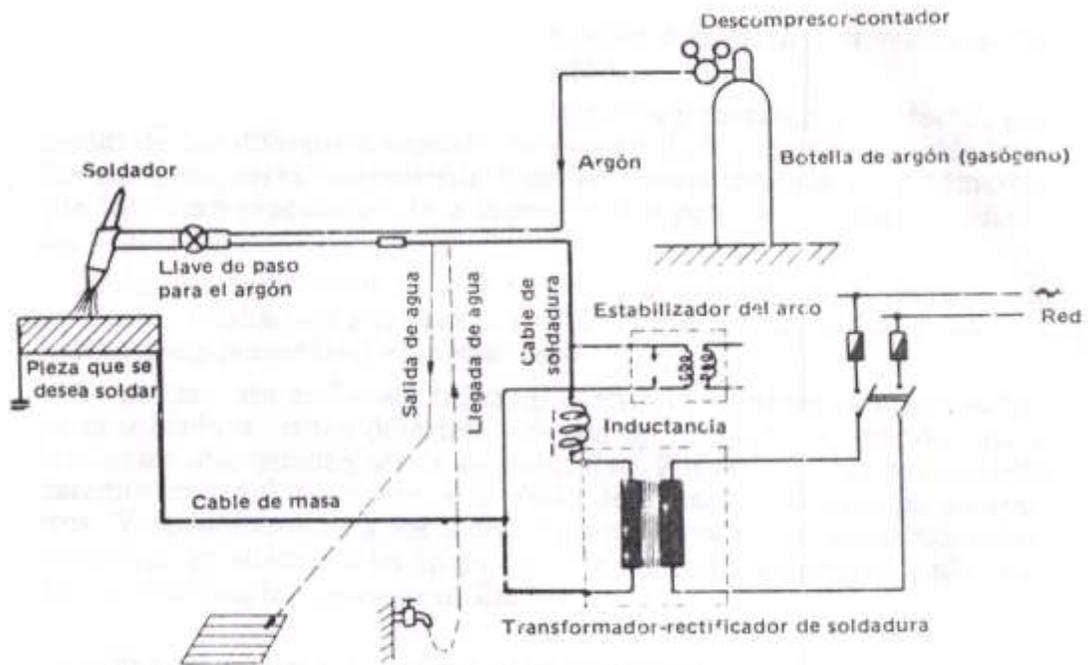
Representación esquemática de una instalación de Soldadura TIG
